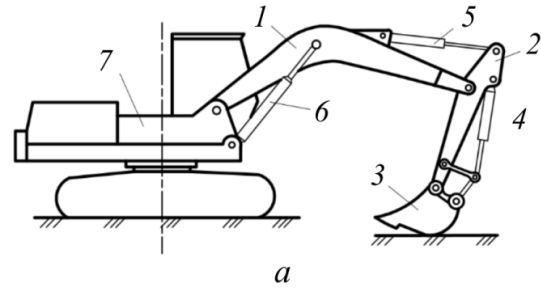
Металоконструкції робочого обладнання одноківшевого екскаватора
